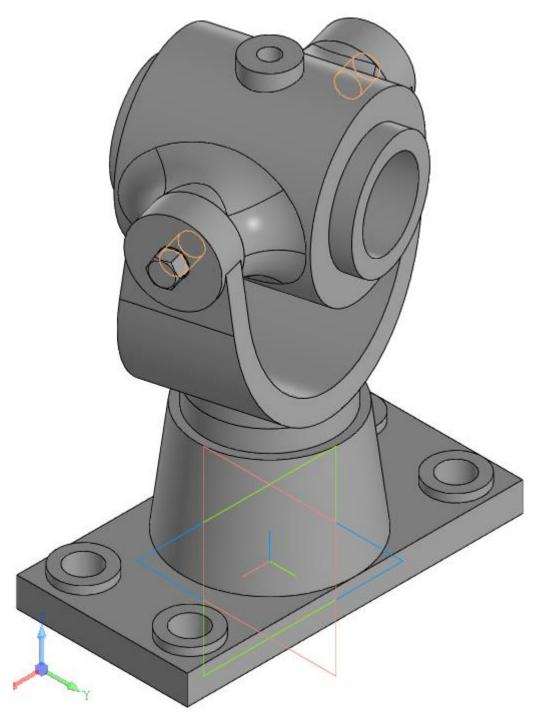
Трехмерная модель сборочной детали, изометрический вид
